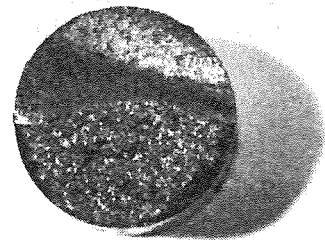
Superfície de fractura dum provete de $\phi=14$ mm, em flexão rotativa com torção.
